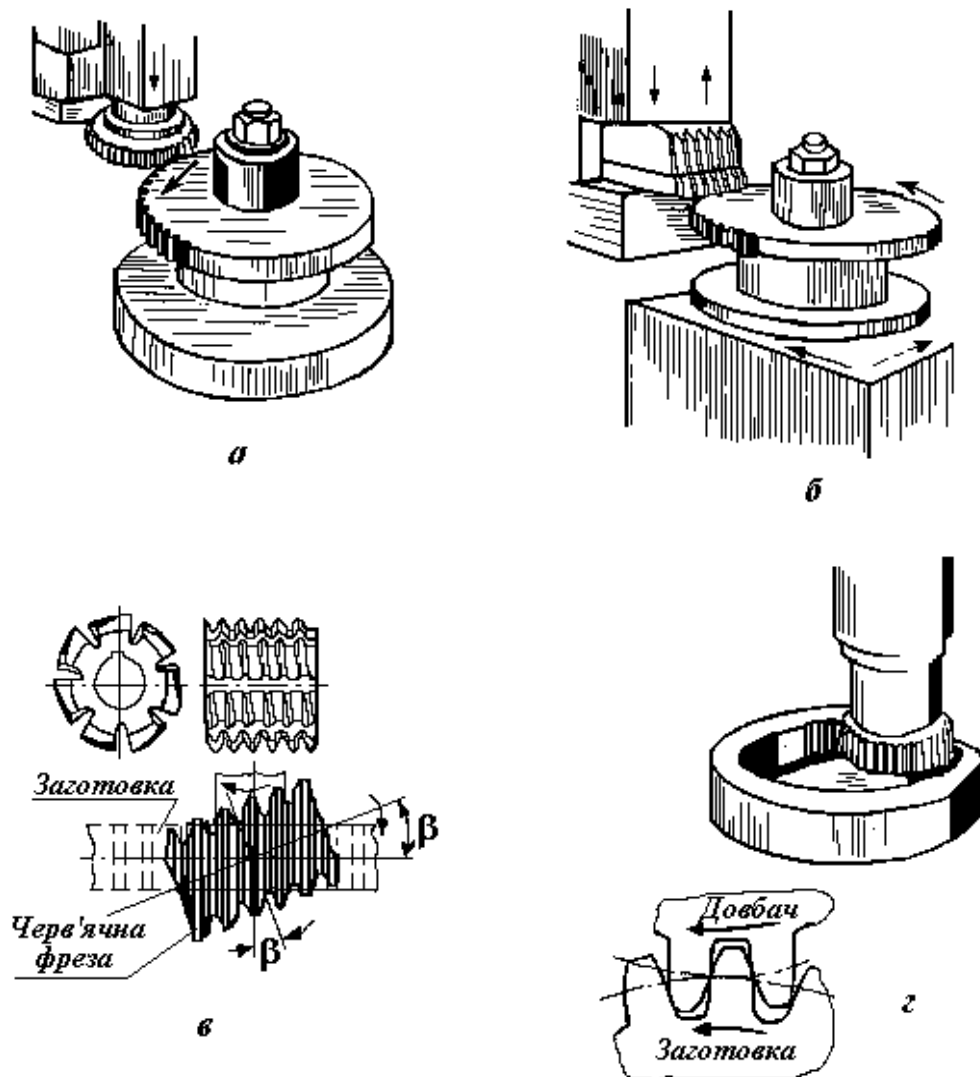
Нарізування зубчастих коліс методом обкатки:
